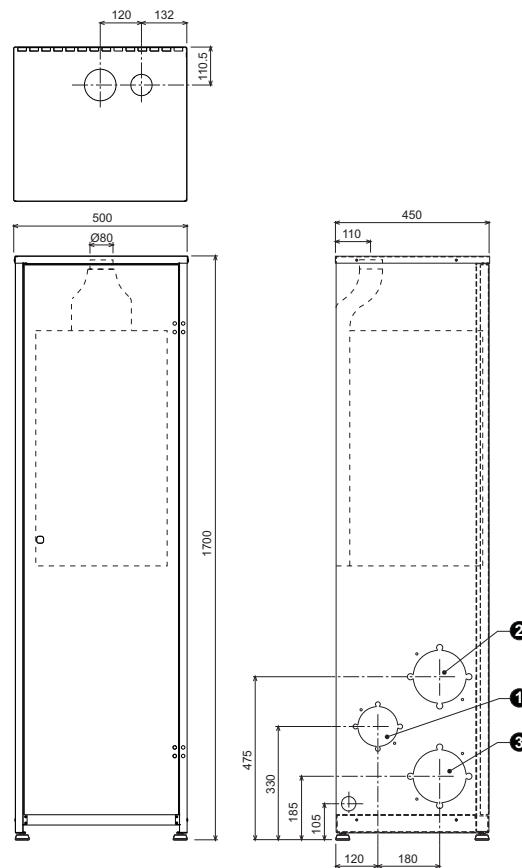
Dimensioni e attacchi modello JOTEK 80 - 125
